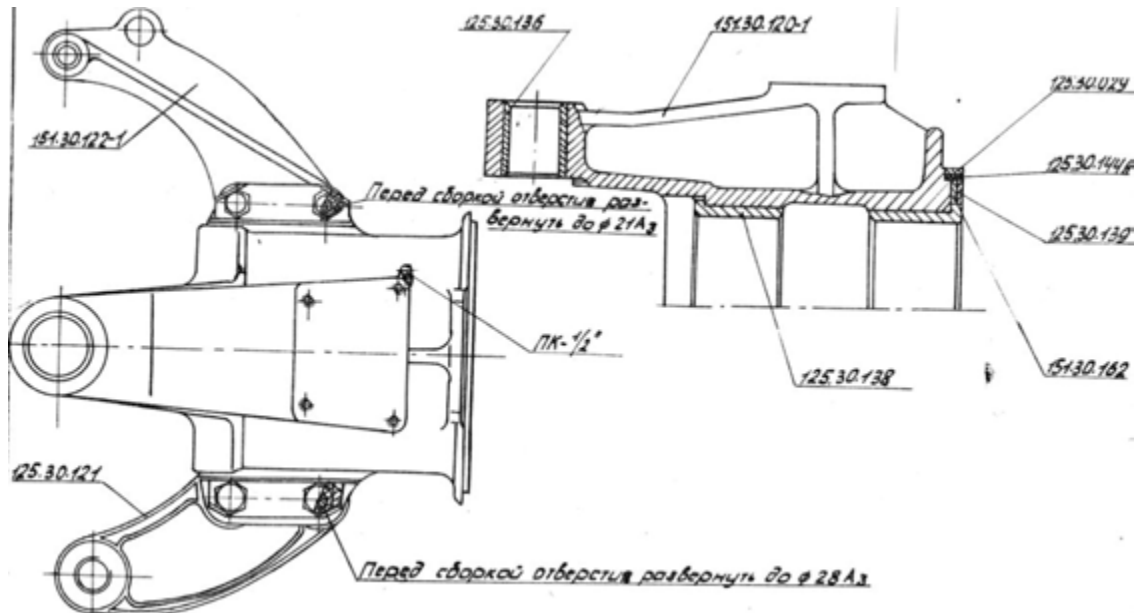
Корпус шарніра в зборі 150К.30.018А
